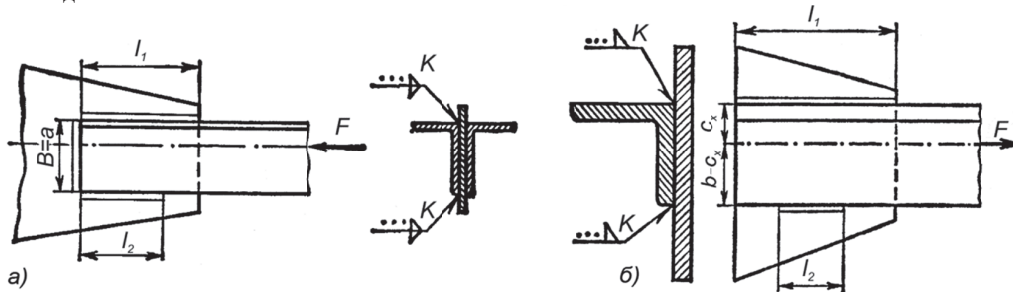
Схема определения суммарной длины сварных швов
